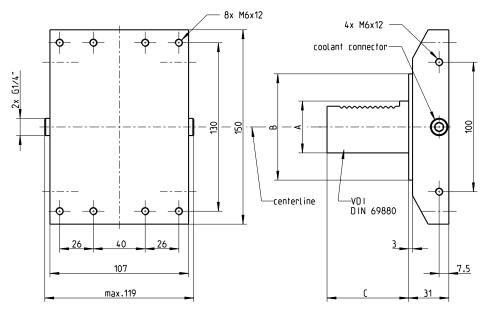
Maschinenadapter mit Zylinderschaft für Scheibenrevolver mit VDI-Werkzeugaufnahme, Typ 9129AB...
